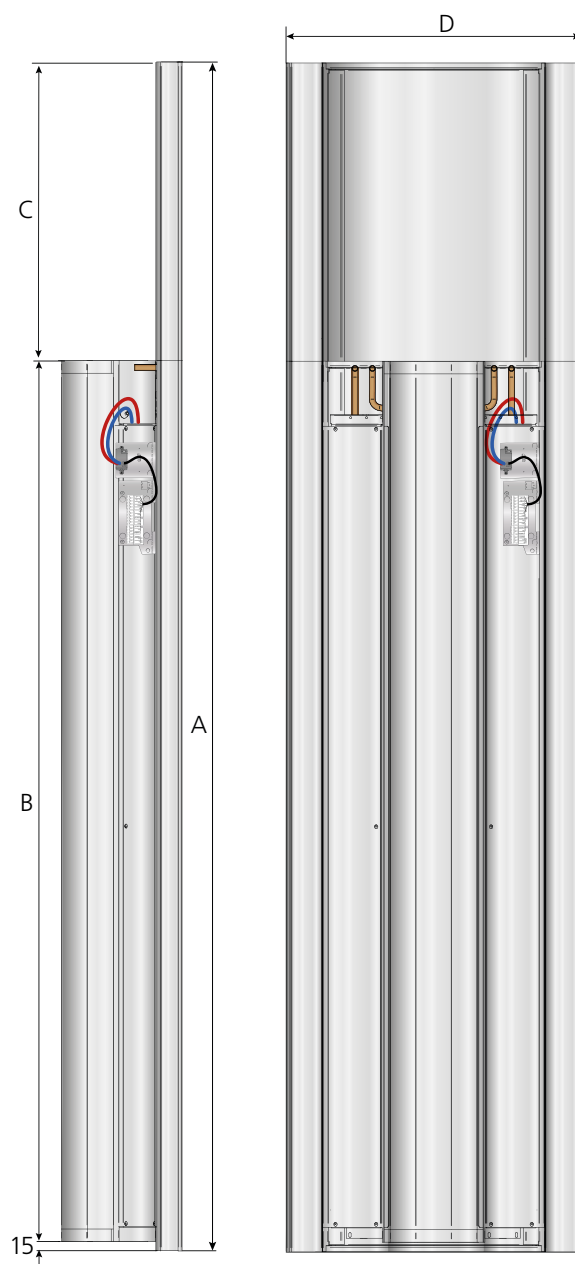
Schizzo dimensionale - Moduli di dimensioni diverse
